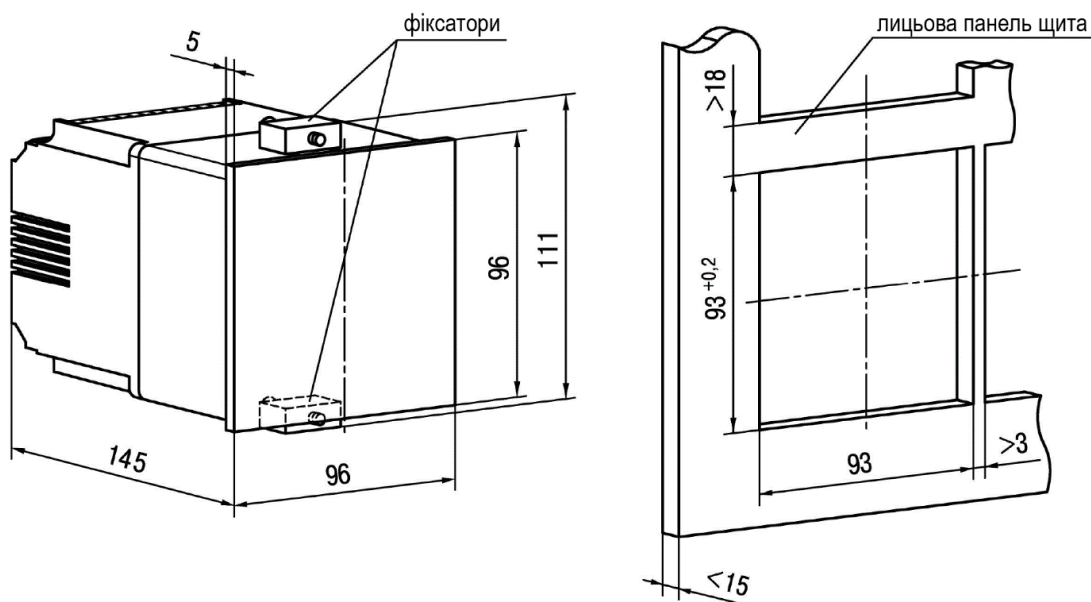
Габаритні розміри корпусу Щ4
